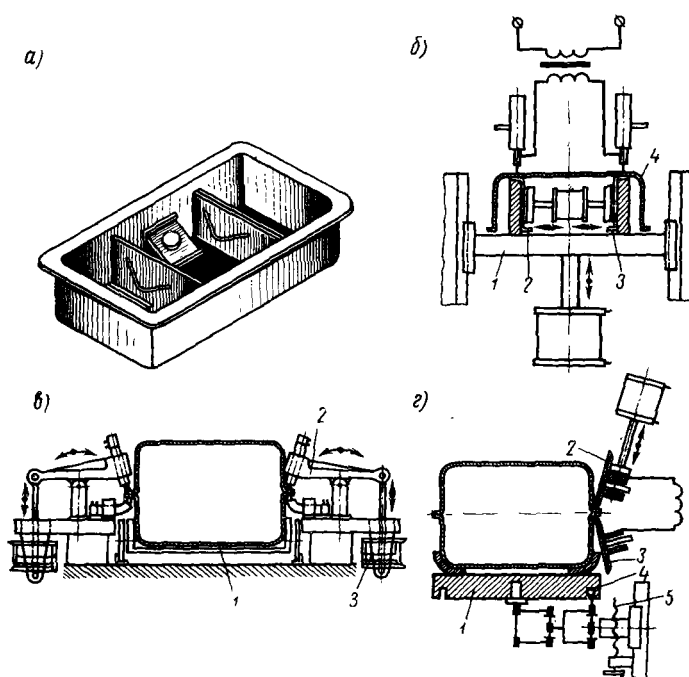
Бензиновый бак и схема машин для его сварки
